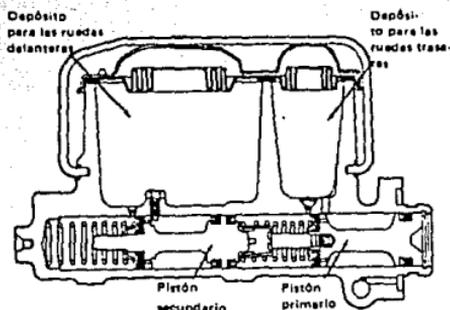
CORTE TRANSVERSAL DE UN CILINDRO MAESTRO TÍPICO
